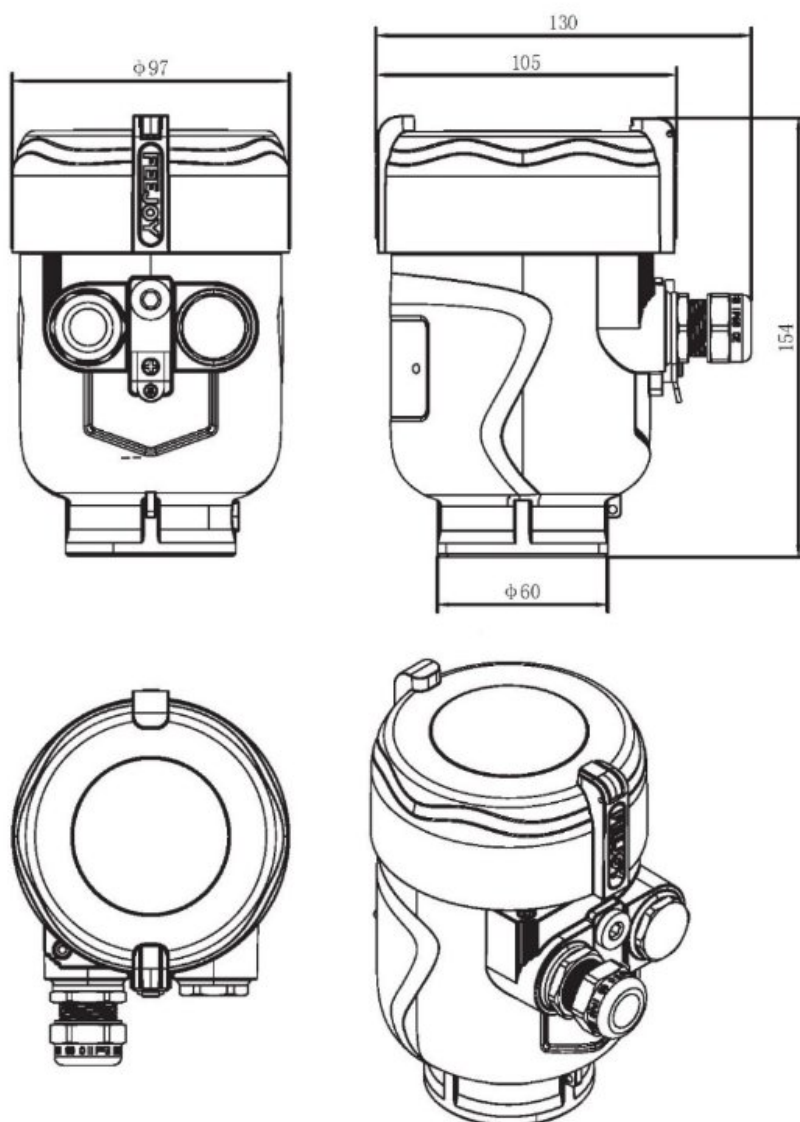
Габаритные размеры корпуса уровнемеров
